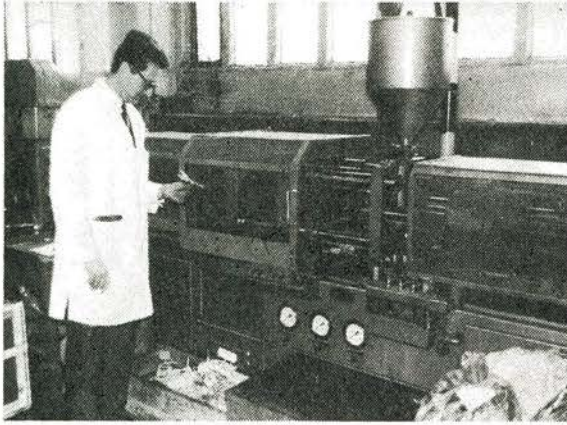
Neue Maschinen zum Kunststoffspritzen erweisen ihre vollen Vorzüge erst beim Einsatz von Mehrfachwerkzeugen, z. B. für die Schwellenfertigung.
